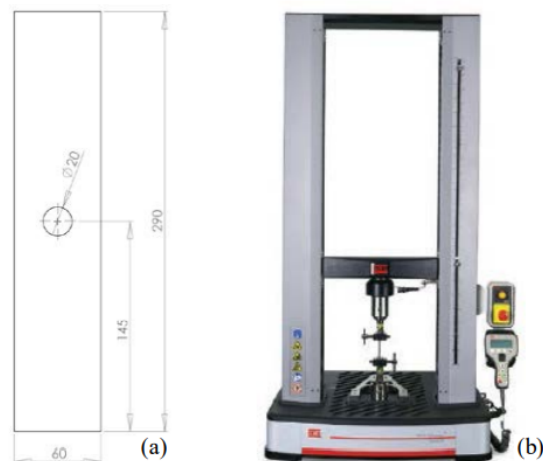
Dimensiones de la probeta empleada para la realización del ensayo mediante DIC (a) y máquina electromecánica empleada para la realización del ensayo (b)
